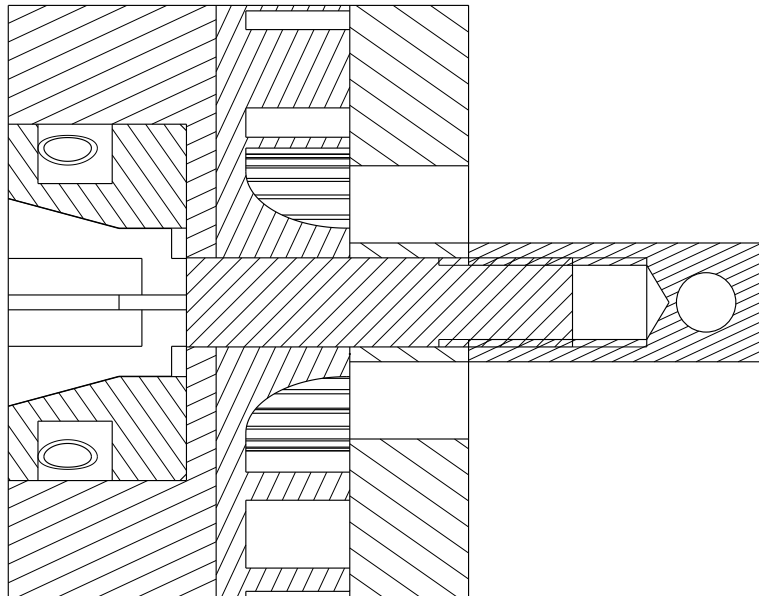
Rotoraufbau (Längsschnitt) mit 3D-gedrucktem Rotorelement *3D_B* (35 Schaufeln; Schaufelhöhe: 3,5 mm).
